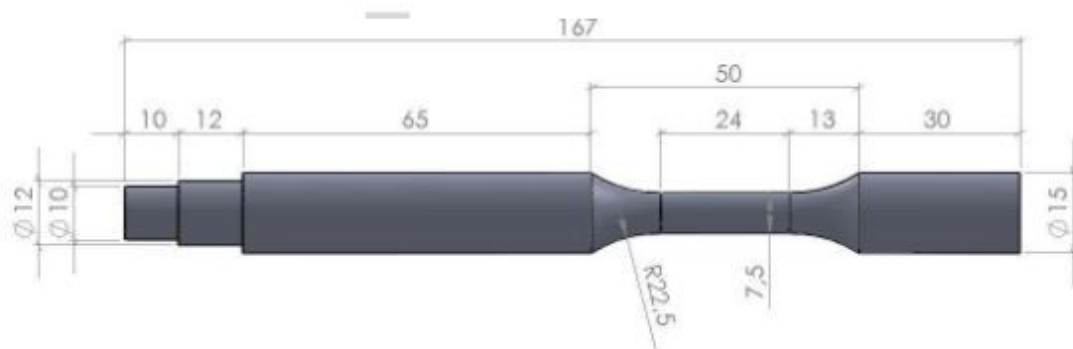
Esquema de la probeta y sus dimensiones. [13]
